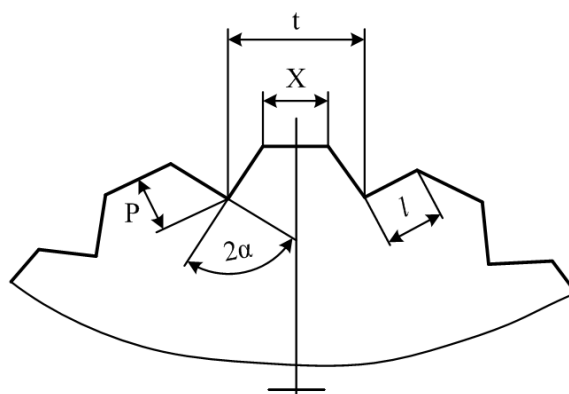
Профиль рифлений на боковой поверхности рабочей части пробивного пуансона
